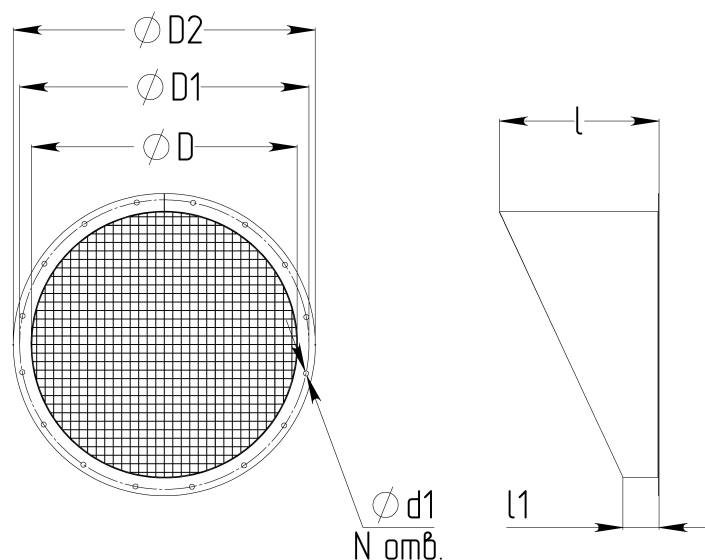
Внешний вид и основные размеры козырька защитного ZKV
